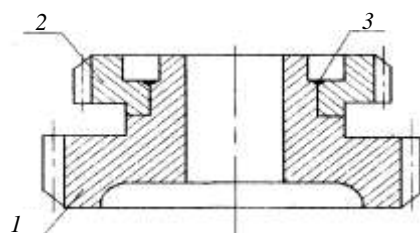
Схема восстановления блока шестерен заменой неисправного зубчатого венца: 1 - основная часть блока, 2 — замененный венец, 3 - сварочный шов
